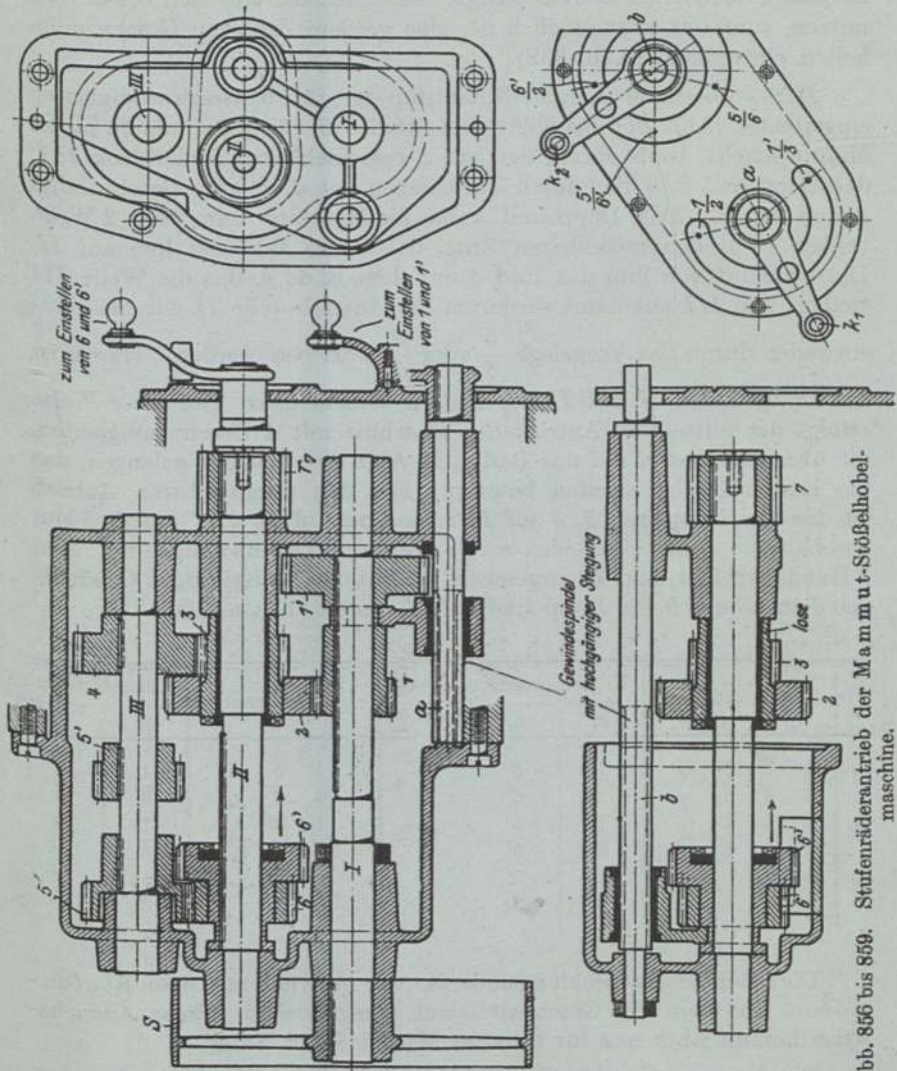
bis 859. Stufenräderntrieb der Mammut-Stößelhelmaschine.
